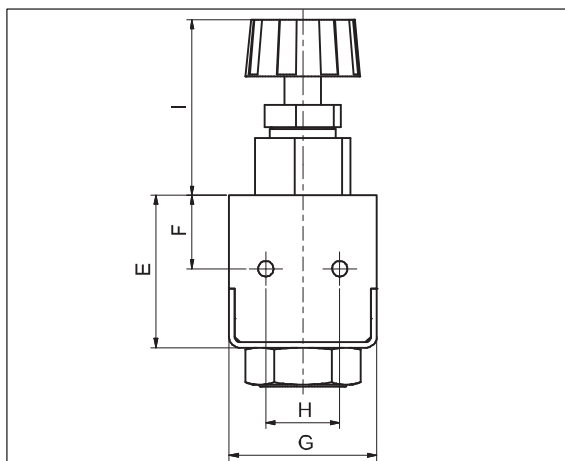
Размеры держателя (с клапаном или без) с резьбовыми отверстиями для опции /QB
